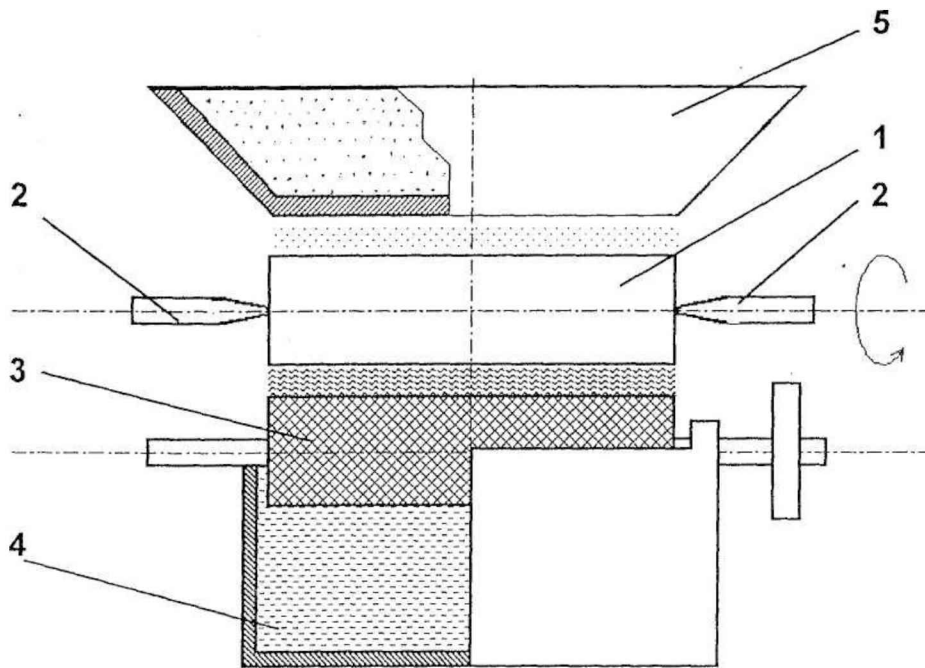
Принципова схема нанесення шлікерної обмазки на відновлювану деталь 1 - відновлювальна деталь; 2 - центри; 3 – обмазувальний валик; 4 - ванна з мастилом; 5 - бункер з порошком
